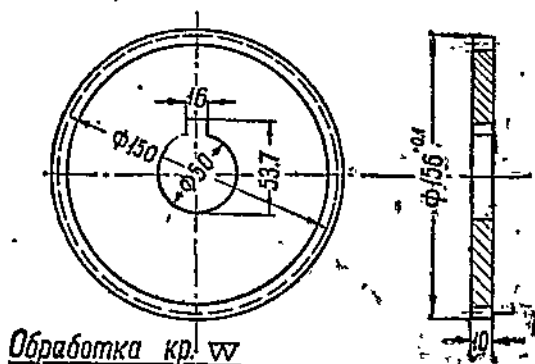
Эскиз шестерни стэнда для испытания цилиндрических зубчатых колес.
